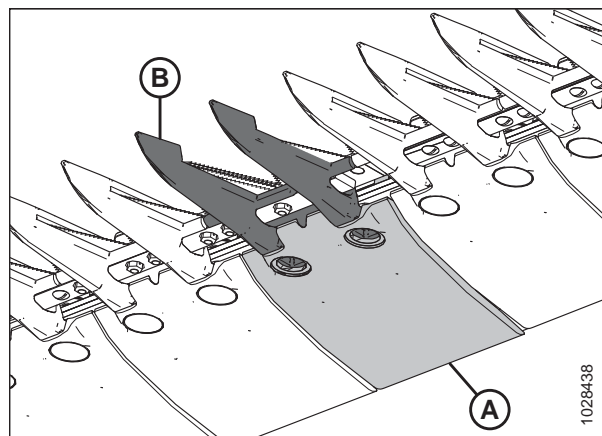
Заостренный центральный противорежущий палец и износная пластина
